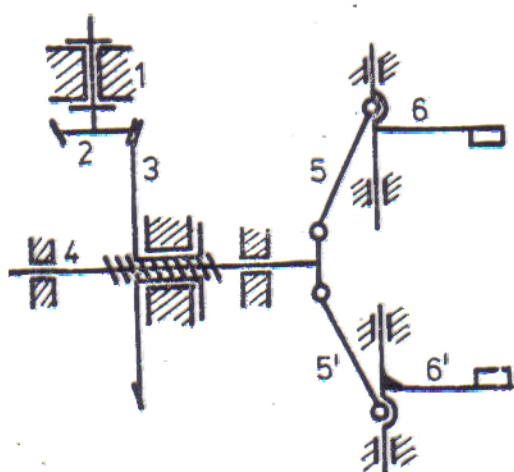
8 Možné principy řešení MÚE typu T4
